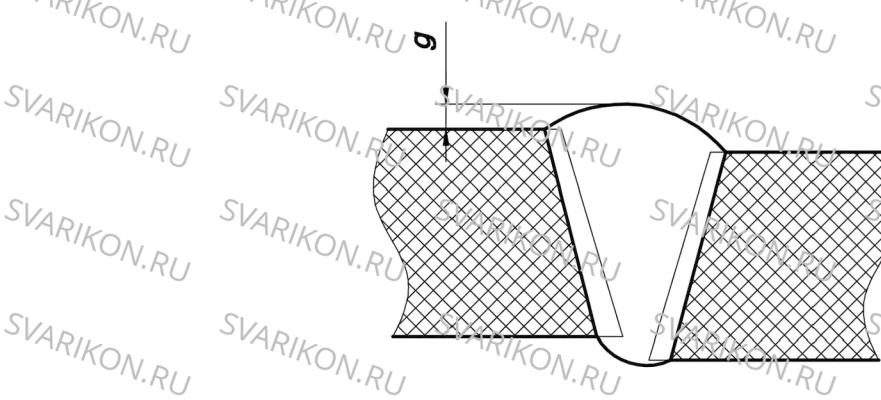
Измерение избыточного материала стыкового сварного шва ( $g$ ) при различном уровне наружных поверхностей деталей, вызванном смещением при сборке соединения под сварку.
